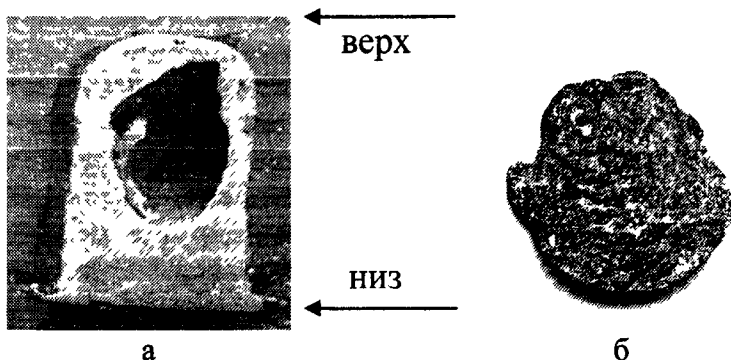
Пористость в образцах сплава МНЦ-15-20 в виде: внутренних пор (а) и разрывов на поверхности отливки (б)
